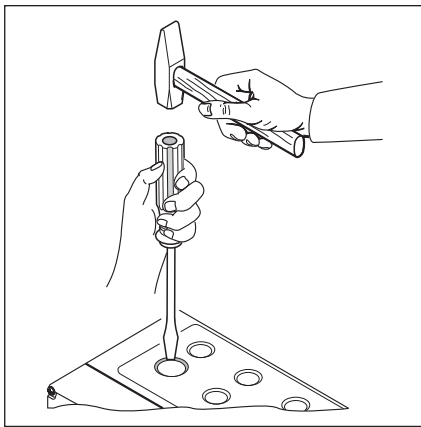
Для дооснащения кабельной арматурой с резьбовым соединением выбивайте предварительно выдавленные места гнезд только при закрытой крышке
